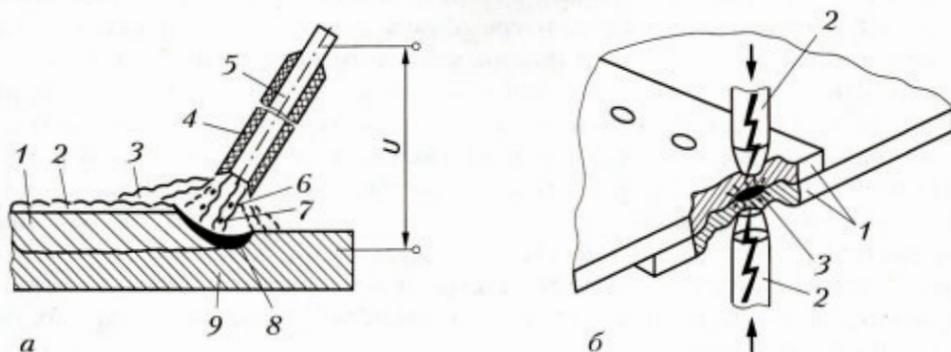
Виды электросварки: *а* – сварка плавящим (металлическим) электродом: 1 – сварной шов; 2 – шлаковая корка; 3 – защитная газовая атмосфера; 4 – электродное покрытие; 5 – электрод; 6 – электрическая дуга; 7 – капли электродного металла; 8 – сварочная ванна; 9 – заготовка; *U* – условные обозначения подвода электрического напряжения; *б* – контактная точечная сварка: 1 – заготовки; 2 – электроды; 3 – сварная точка
